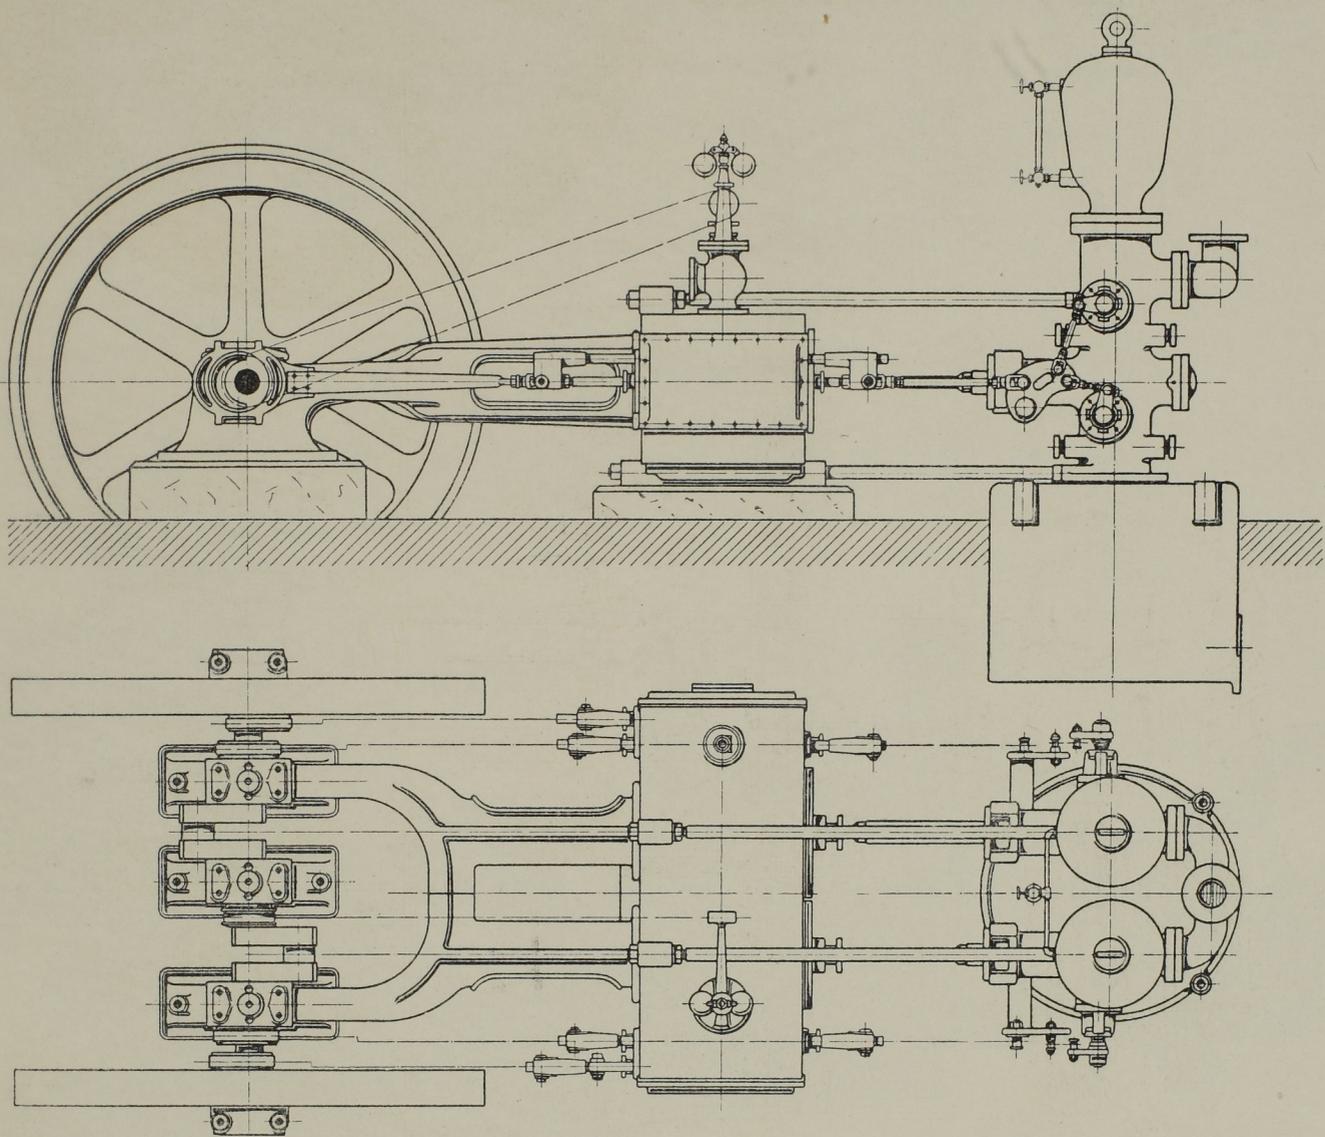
Seitenansicht und Grundriss. Massst. 1:32.
